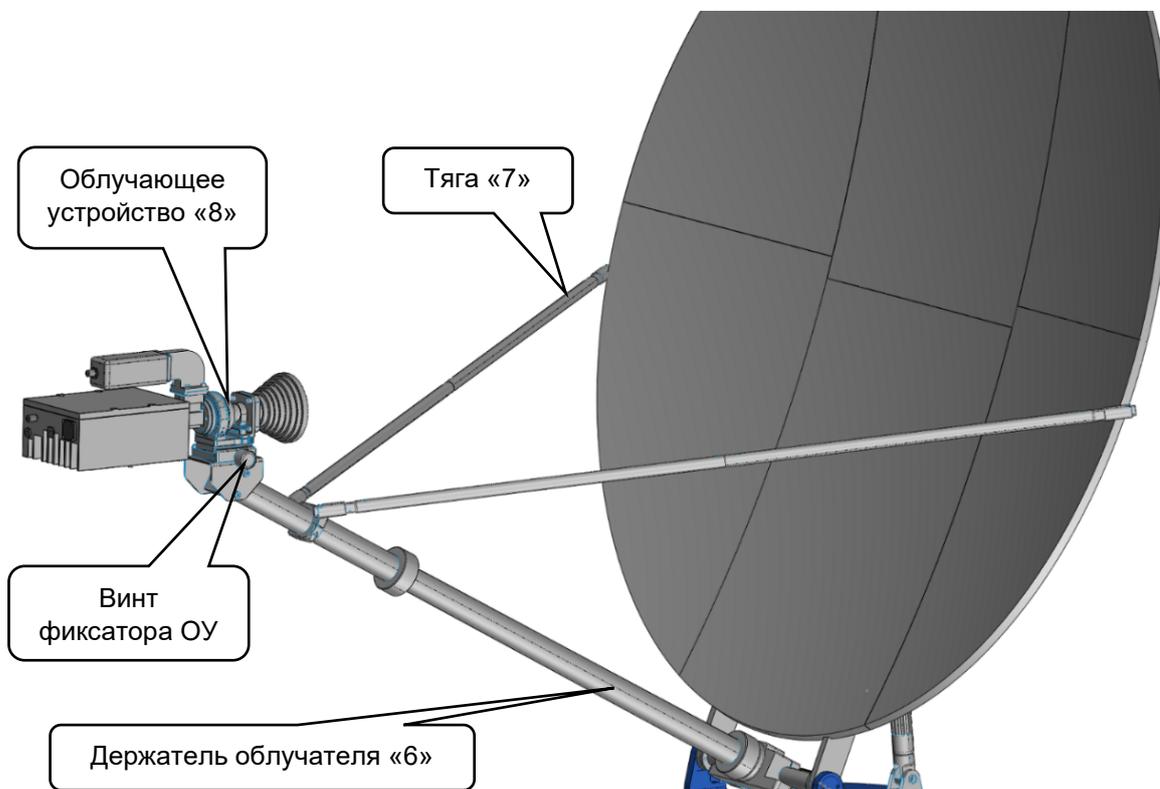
д – Сборка тяг и держателя с ОУ
